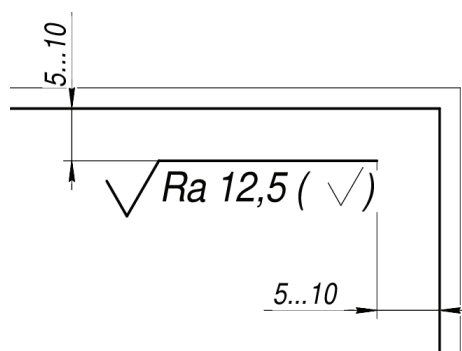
Обозначение шероховатости, одинаковой для группы поверхностей детали
